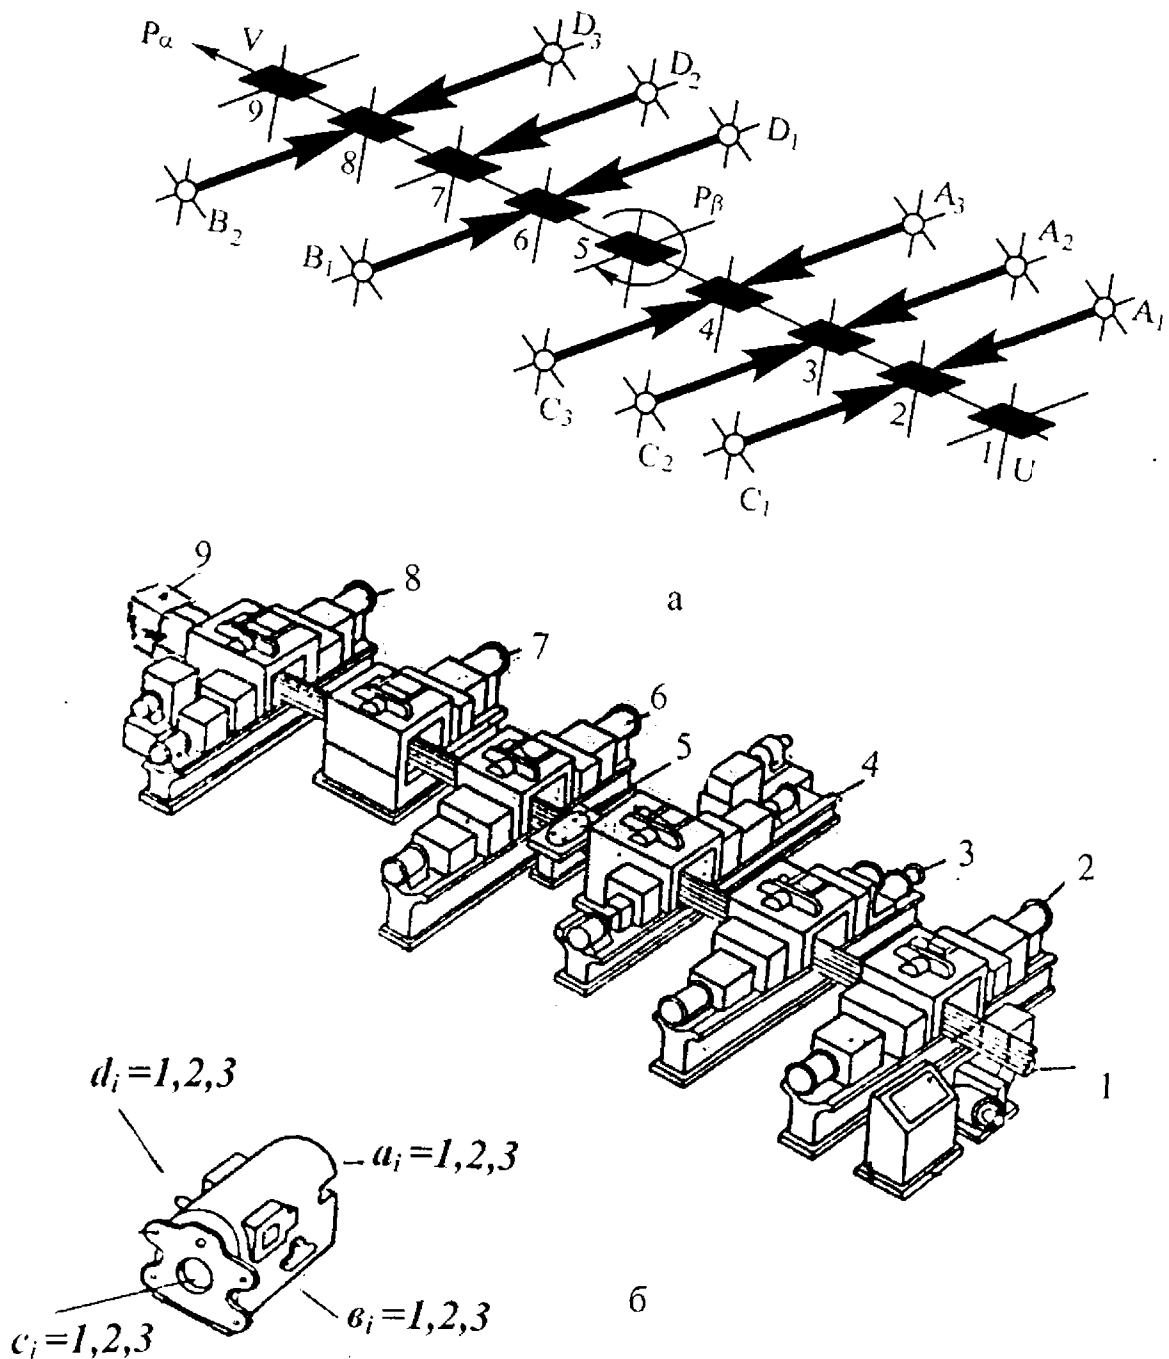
Операторна схема АЛ, яка складається з агрегатних верстатів.
